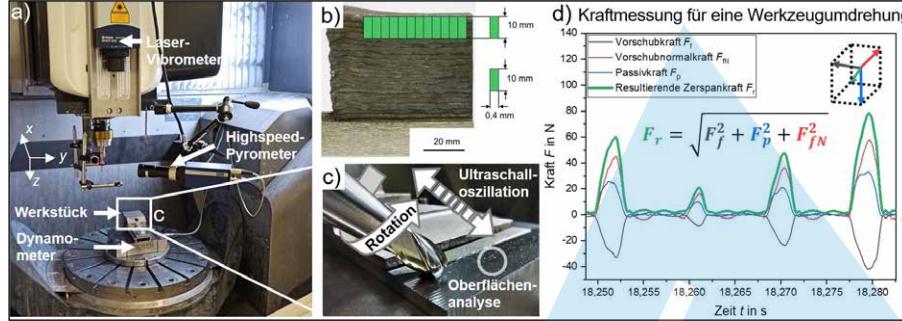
Aufbau Fräsversuche (a), Probenentnahme/-geometrie (b), Detail Werkzeugeingriff (c), Kraftanalyse eine Werkzeugumdrehung (d) [11].
